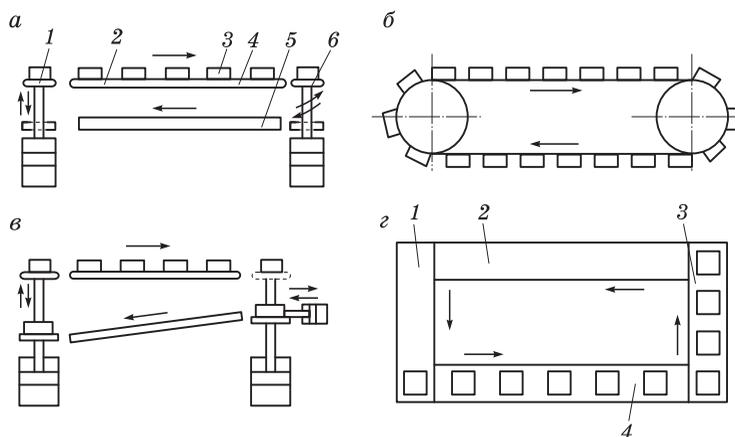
Схемы устройств возврата приспособлений-спутников
